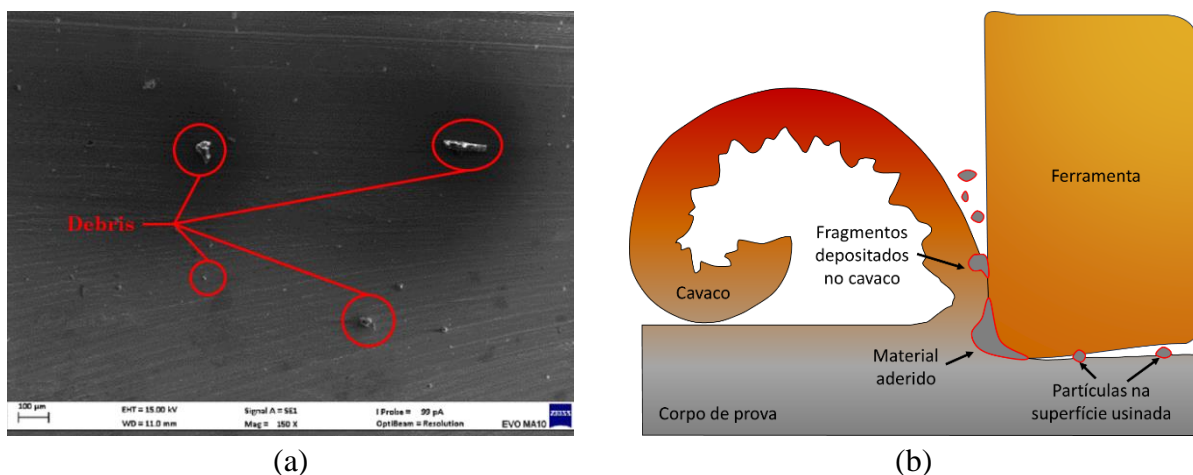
(a) Superfície do corpo de prova gerada pelo passe 5; (b) Formação de debris encontrados na superfície do corpo de prova.
